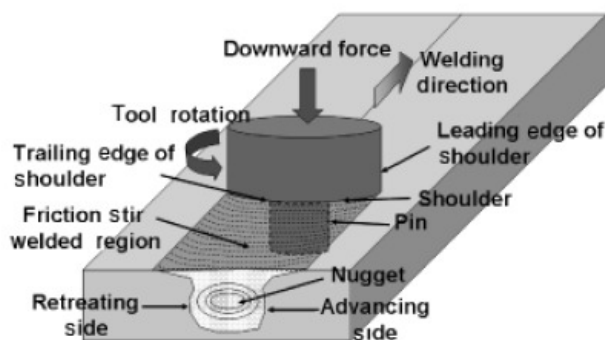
Desenho esquemático do processo de soldagem “*Friction Stir Welding*”.
